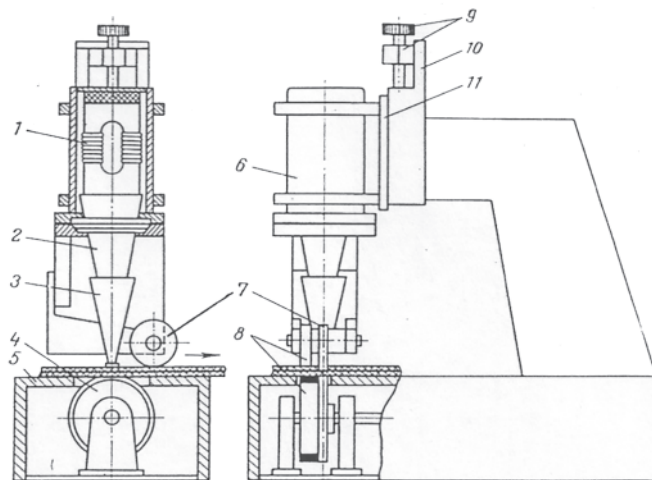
Сварочная машина УПШ-12: 1 – преобразователь; 2 – трансформатор упругих колебаний; 3 – волновод-инструмент; 4 – опора-ролик; 5 – рабочий стол; 6 – ограждение преобразователя; 7 – прокатывающий ролик; 8 – протягивающие ролики; 9 – установочный винт и гайка; 10 – станина; 11 – подвижная панель.
